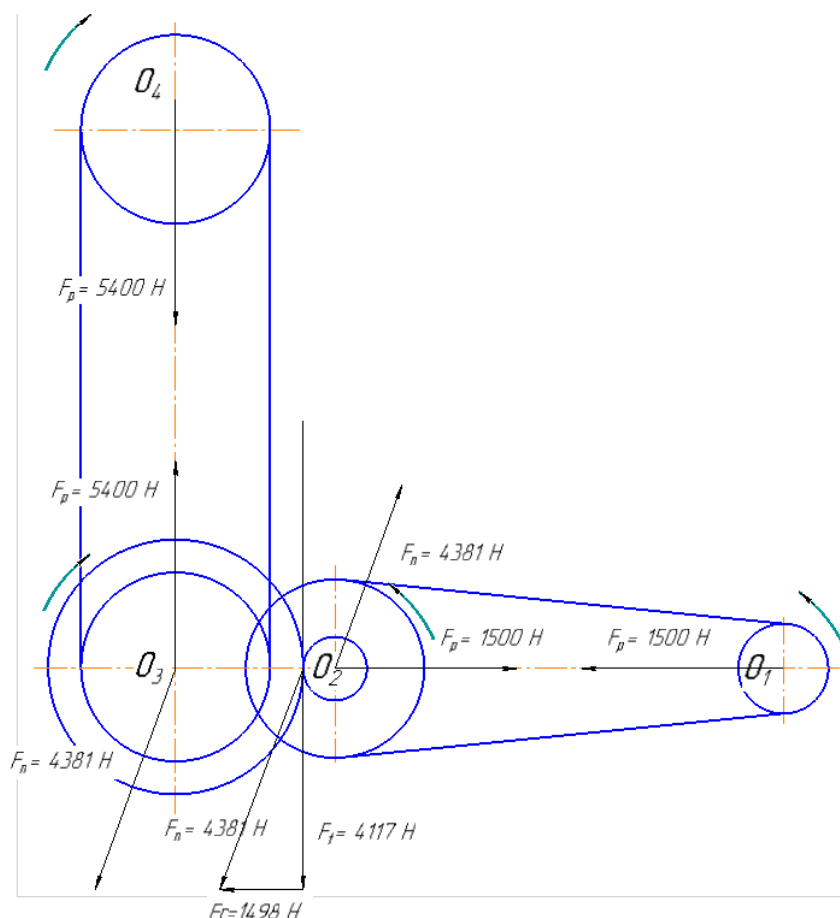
Компоновочная схема свертки коробки скоростей
